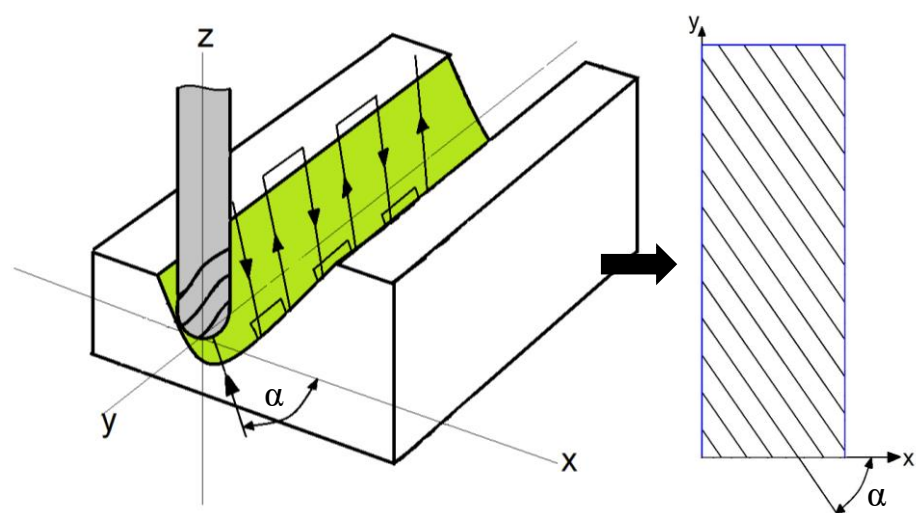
Схема фрезерования формообразующей поверхности с траекторией фрезерования под углом  $\alpha$
